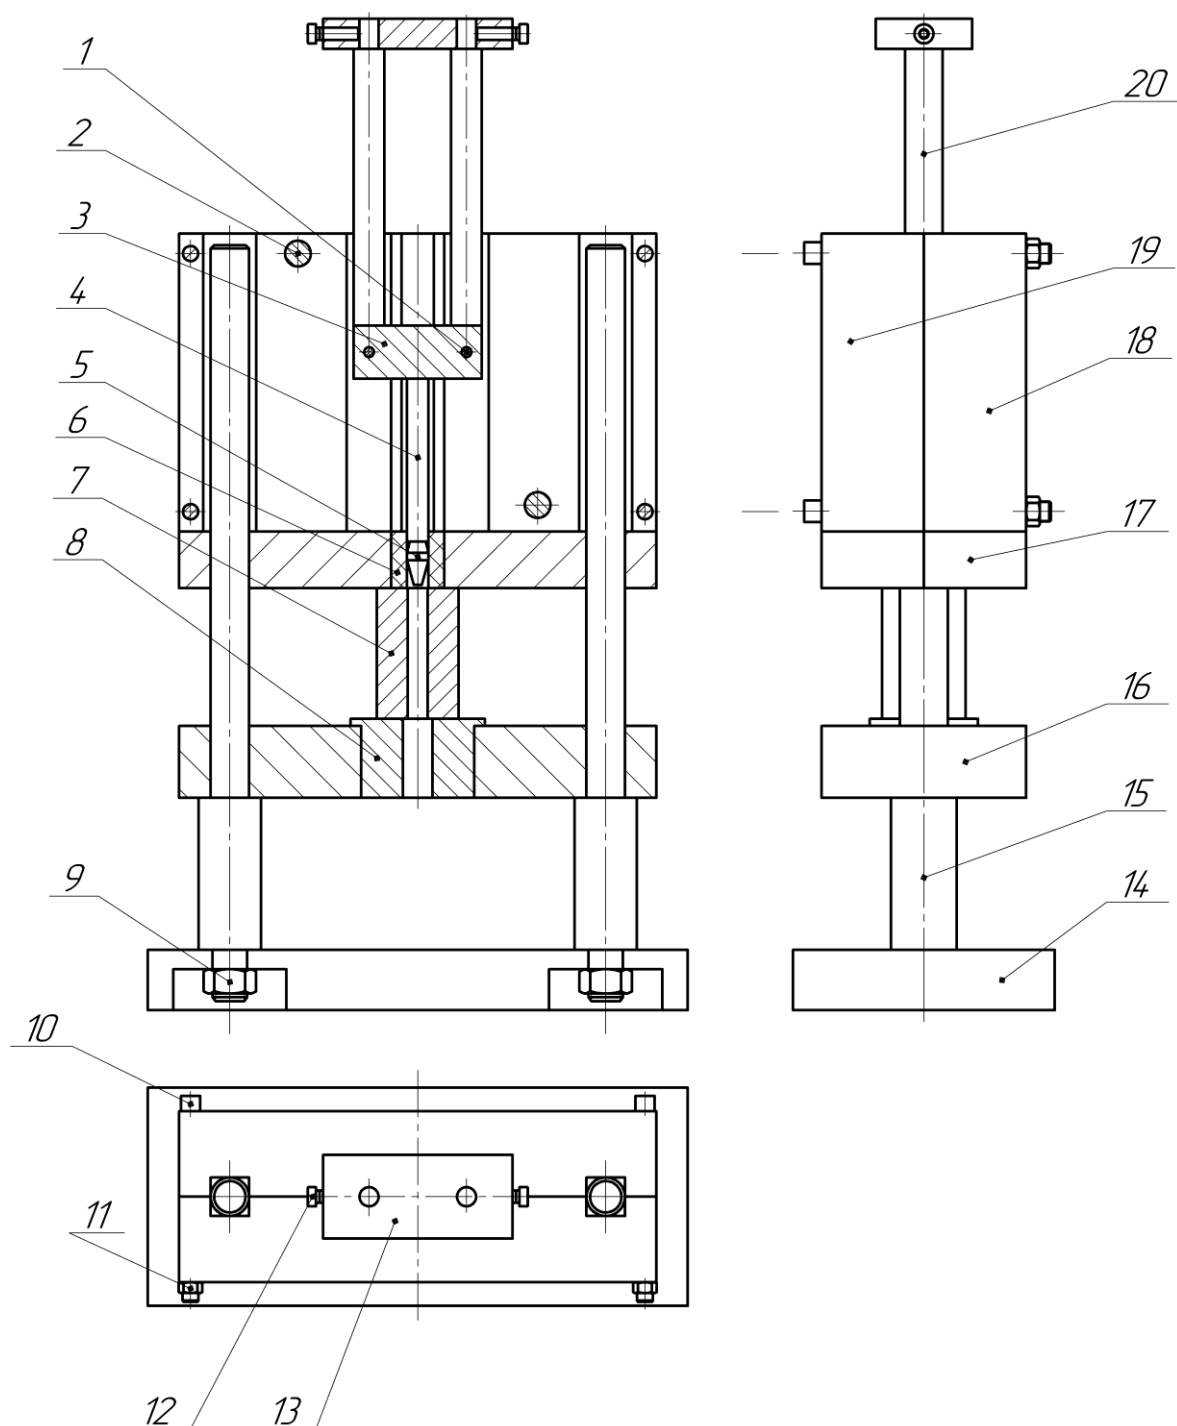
Приспособление для дорнования глубоких отверстий малого диаметра
